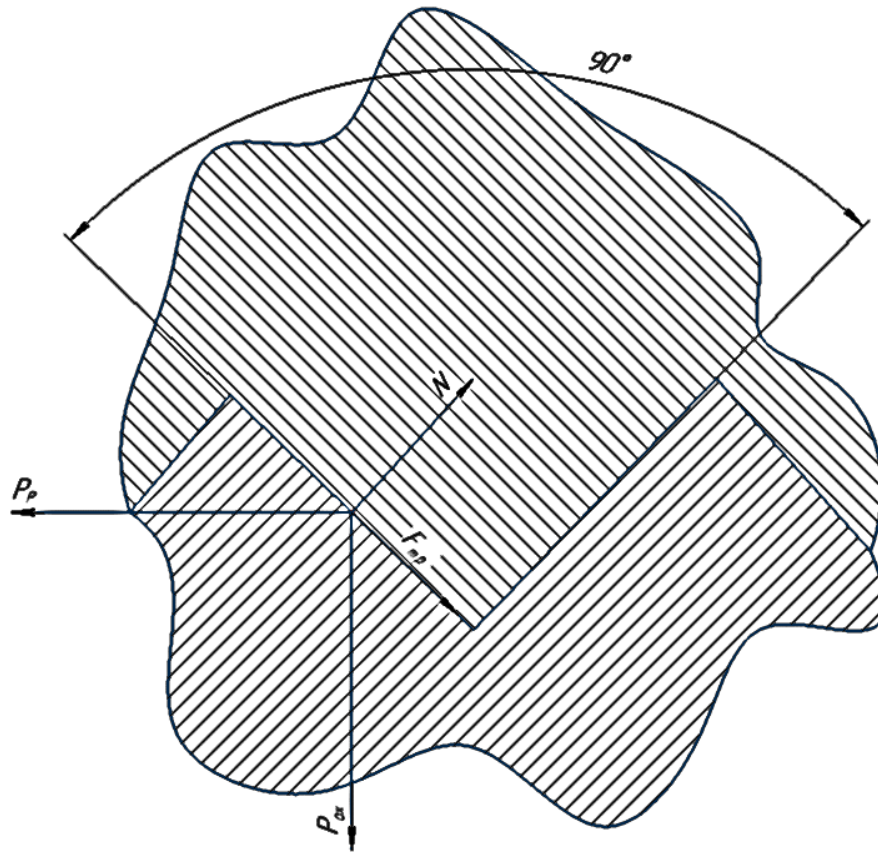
Схема дії сил в з'єднанні корпус-змінна головка
